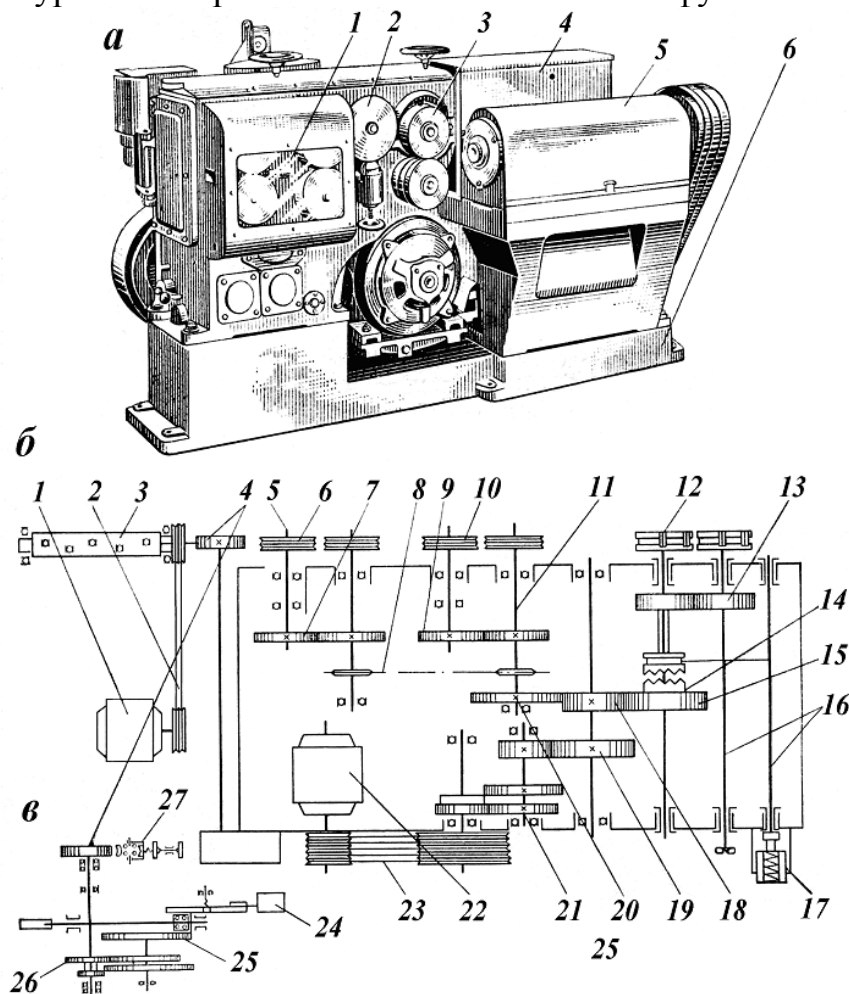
Станок для одновременной правки и резки арматурной стали с непрерывной подачей: а – общий вид; б – кинематическая схема
